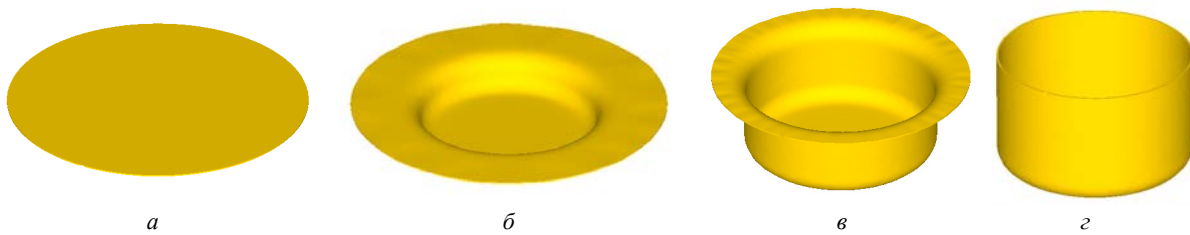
Заготовка на різних етапах першої витяжки з притисканням фланця: а – заготовка, б, в – проміжні стадії витяжки, г – готовий напівфабрикат
